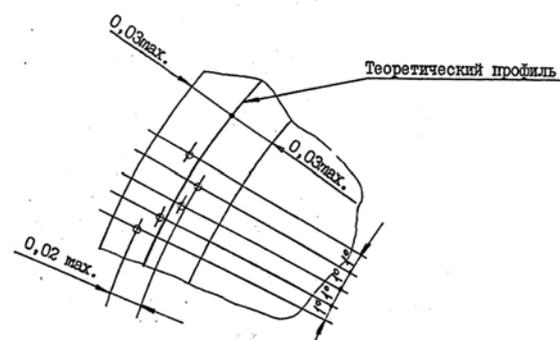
а. Допускаемые отклонения профиля кулачков для распределительных валов ВАЗ 2101-1006010; -100601020 и 212131006010 в зоне А
